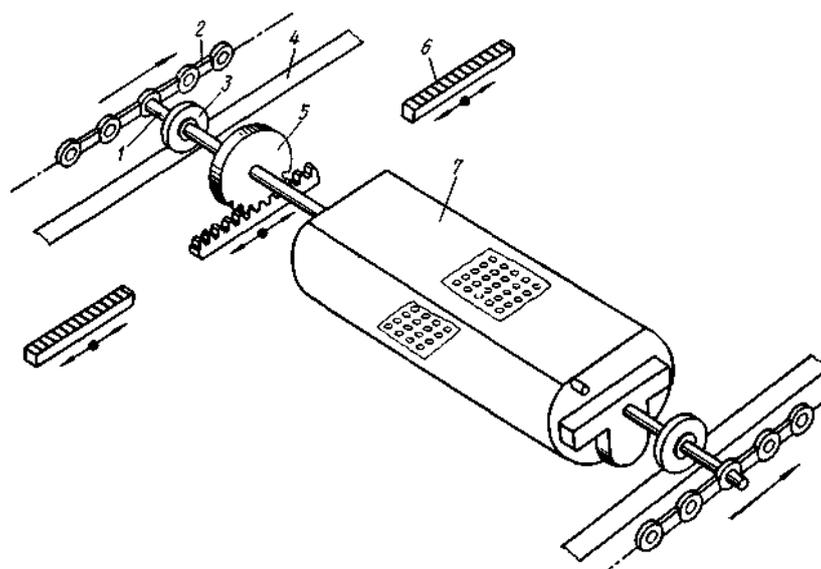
Схема перемещения цилиндрической кассеты в сушилке фирмы «Ролинокс»:
